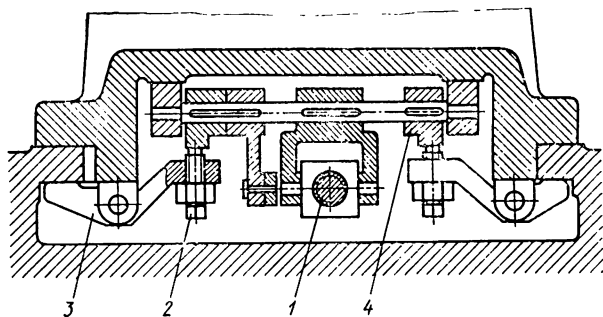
Рычажно-винтовой механизм крепления перемещаемой станины к основанию одностоечного станка с консольной поперечиной:
